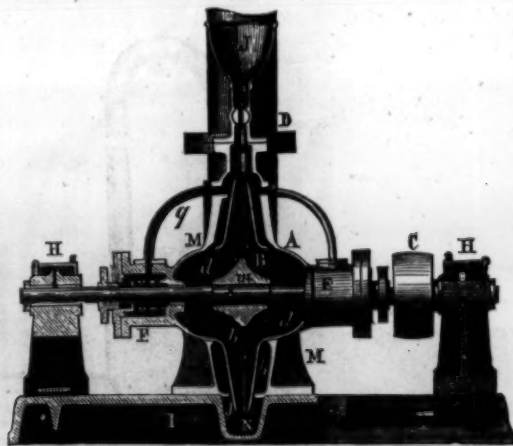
Coupe de la pompe Neut et Dumont, perpendiculaire au plan de rotation de la turbine.
